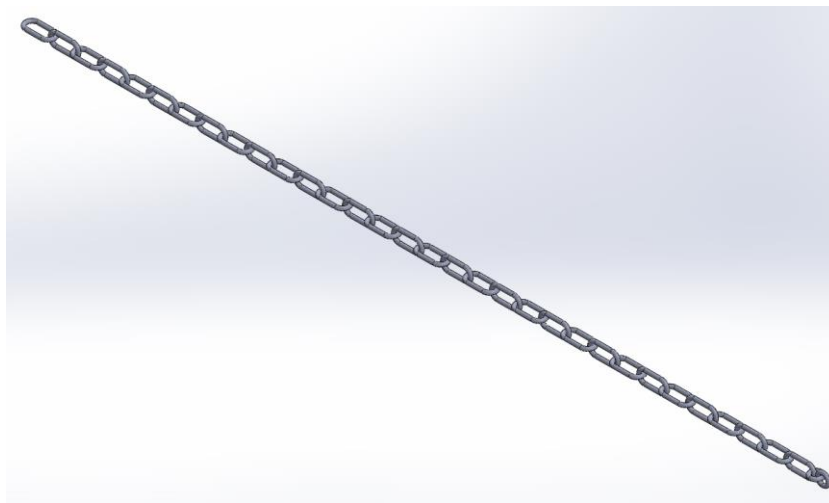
Sub-ensamblaje 01-13-00, respectivo a la Cadena entre la viga elevadora y el pistón del cilindro principal de la máquina de vapor de Newcomen. Vista general completa.
